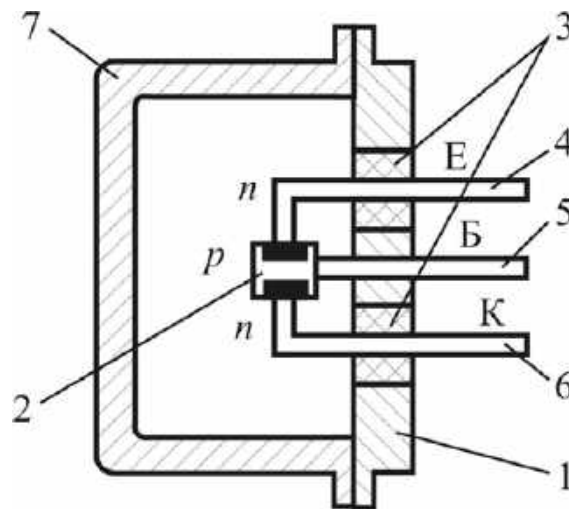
Конструкція малопотужного біполярного транзистора: 1 – основа; 2 – кристал напівпровідника; 3 – ізолювальні втулки; 4, 5, 6 – виводи емітера Е, бази Б, колектора К; 7 – корпус
